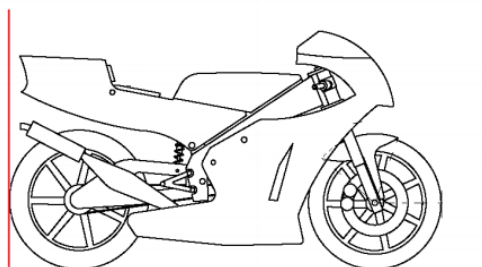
Distancia libre entre pavimento y moto [6]
